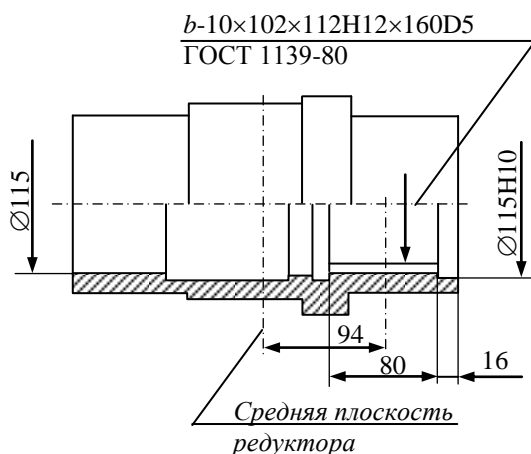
П7 Присоединительные размеры полого вала редуктора 1ЦЗУ-250
